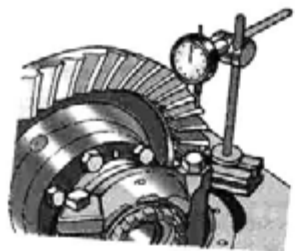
Проверка бокового зазора в зацеплении зубьев шестерен главной передачи (мост с балкой типа банджо)
